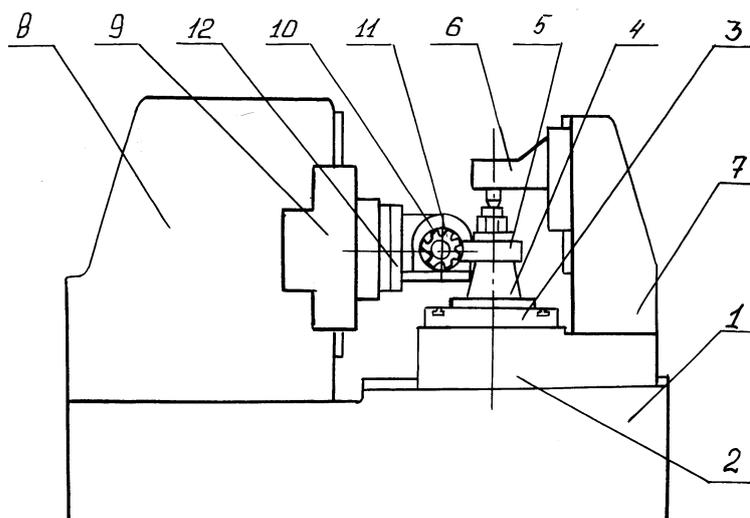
Компонновка зубофрезерного станка модели 5К32
